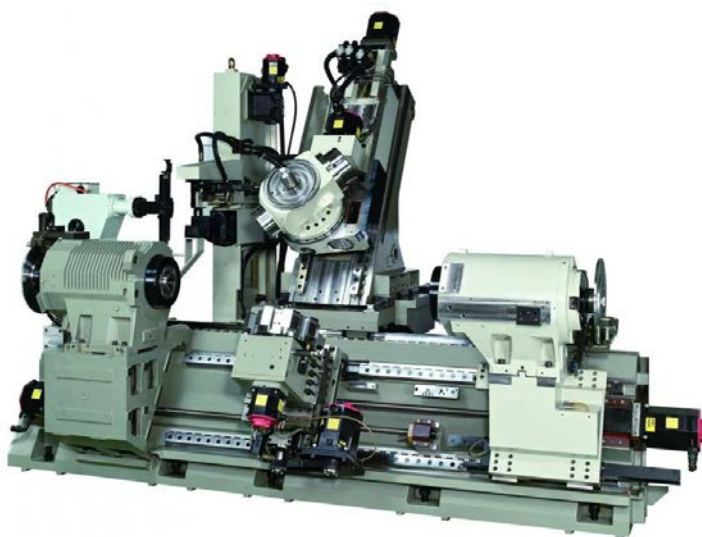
Токарно-фрезерный станок с ЧПУ
